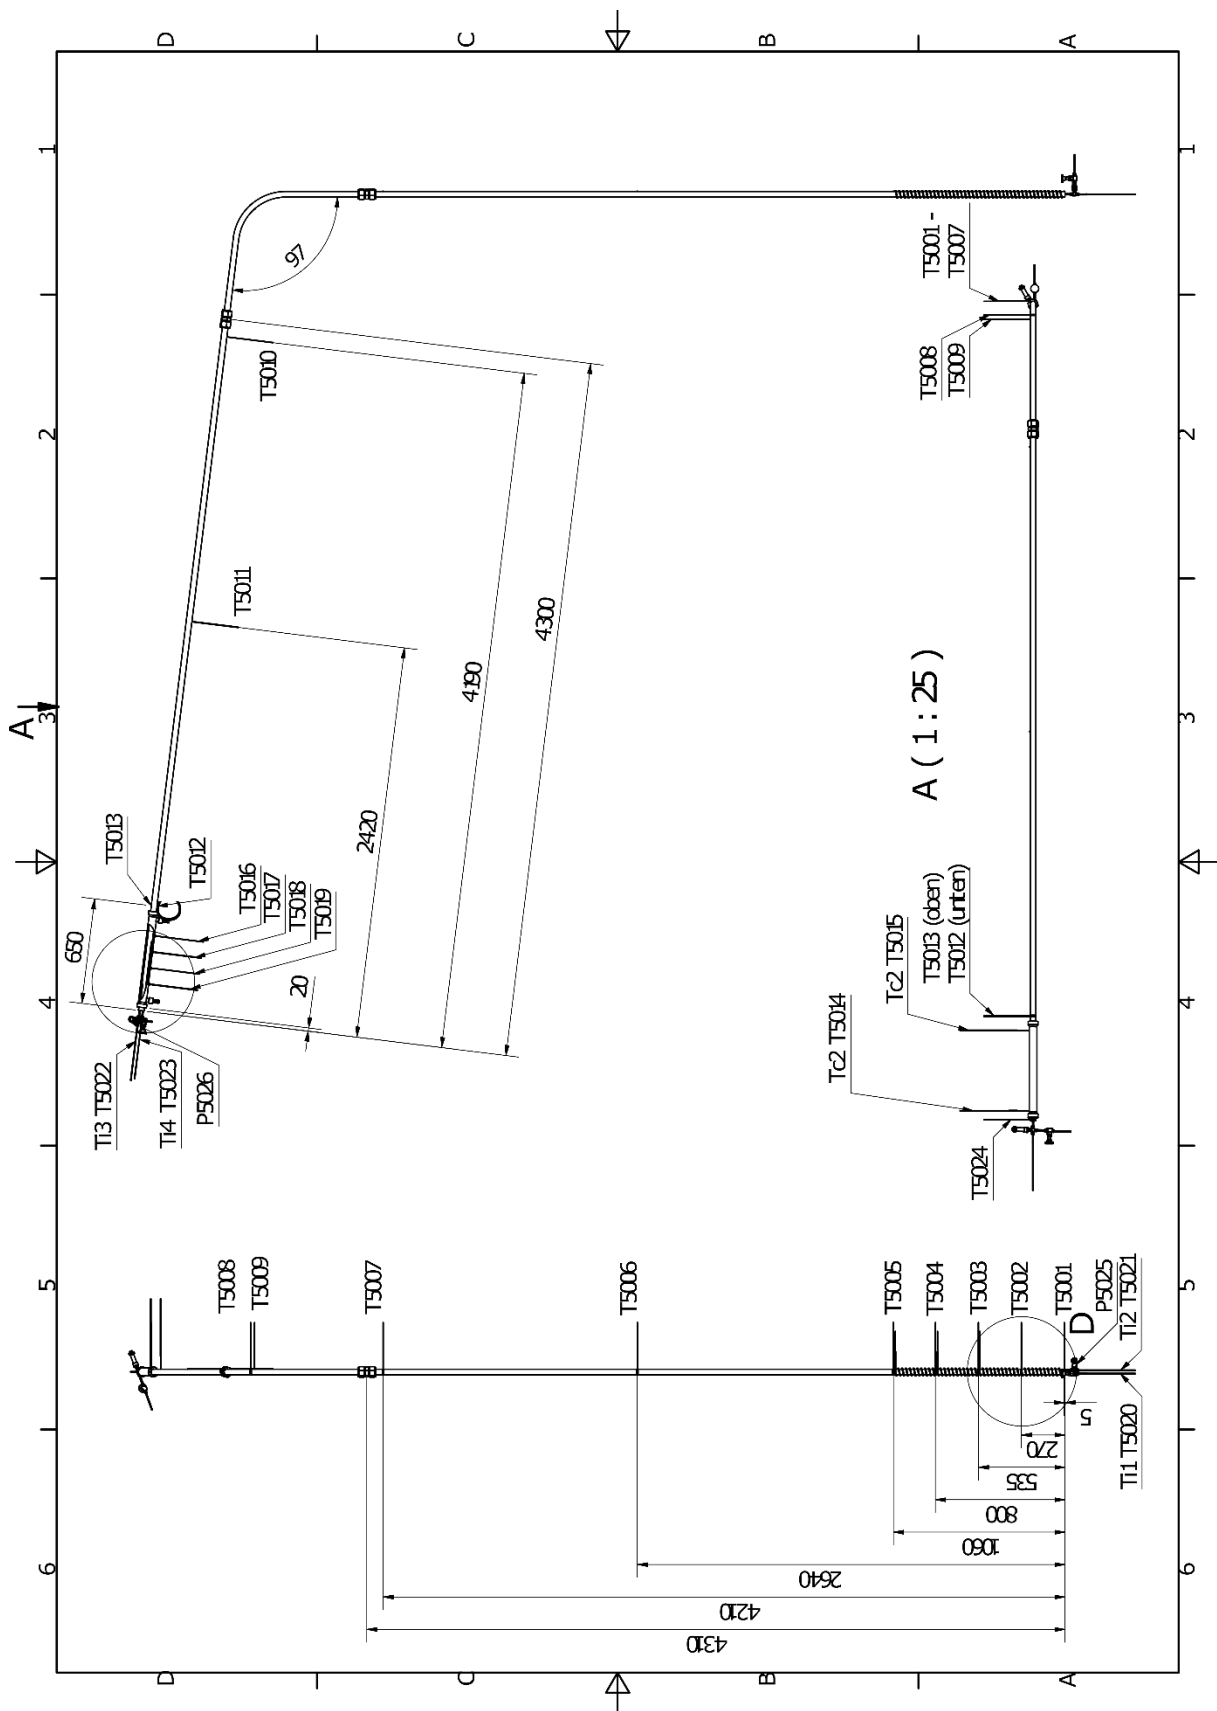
Technische Zeichnung gekrümmtes Thermosiphon Laborrohr $d_i=32$ mm
